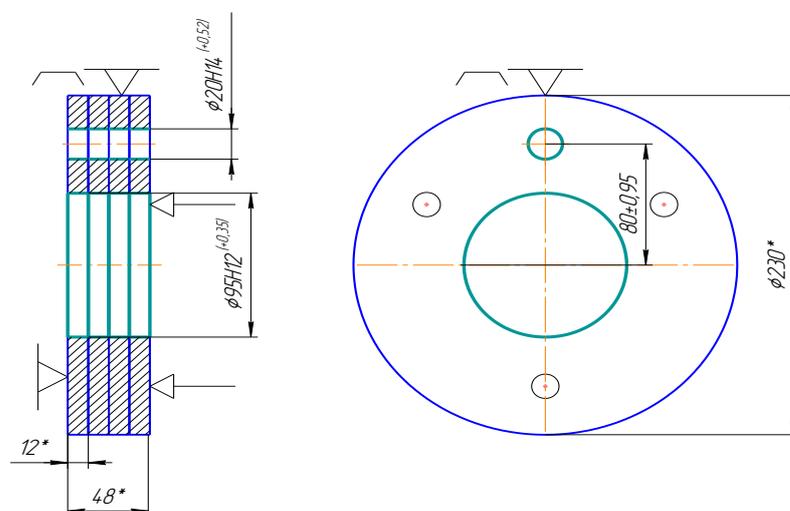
Схема установки для горизонтально-расточной операции 005
